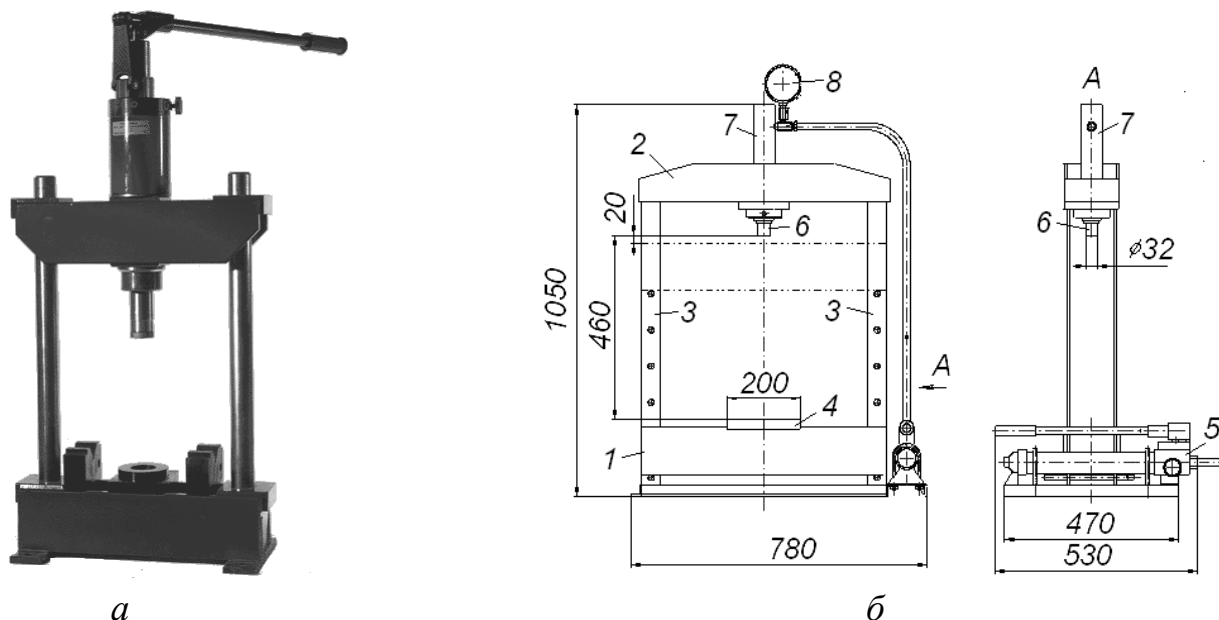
Зовнішній вигляд (а) та принципова схема (б) гідравлічного пресу типу ПГ-10. 1 – нижня станина; 2 – верхня станина; 3 – направляючі; 4 – піддон для прес-форм; 5 – система кріплення піддону; 6 – пуансон; 7 – ручний гідравлічний насос; 8 – манометр
